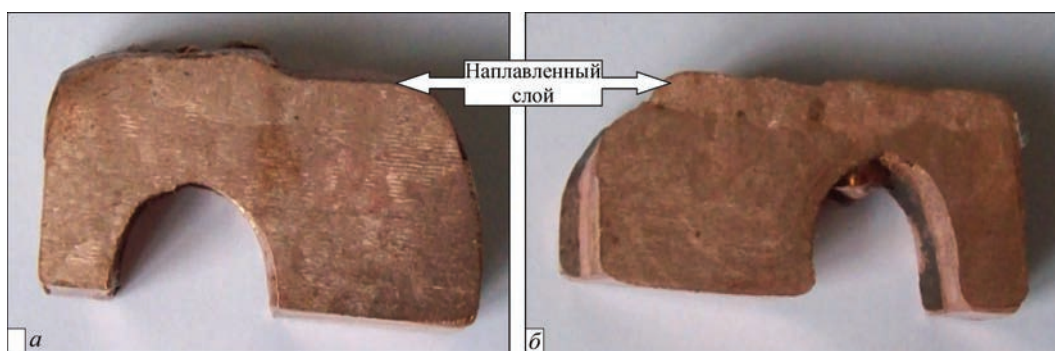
Внешний вид наплавленных участков: а — гелиево-дуговая наплавка; б — покрытыми электродами
